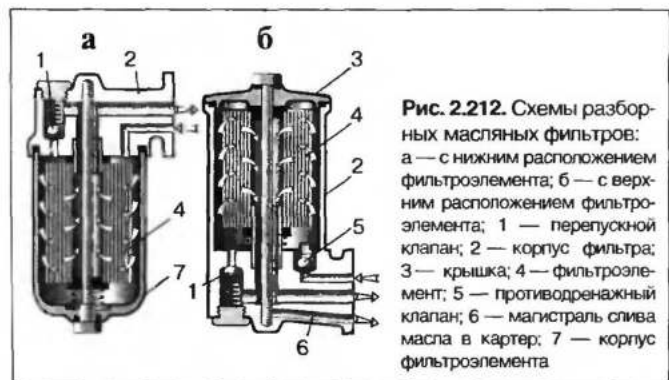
Схемы разборных масляных фильтров: а — с нижним расположением фильтроэлемента; б — с верхним расположением фильтроэлемента; 1 — перепускной клапан; 2 — корпус фильтра; 3 — крышка; 4 — фильтроэлемент; 5 — противодренажный клапан; 6 — магистраль слива масла в картер; 7 — корпус фильтроэлемента
